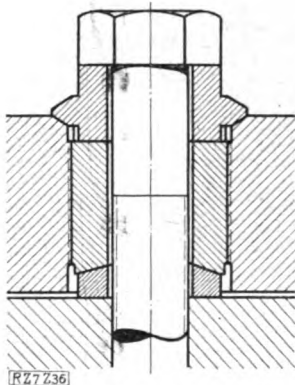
Schraube zur Verankerung der Gewindebüchsen am Kastenbett, Abb. 35.
